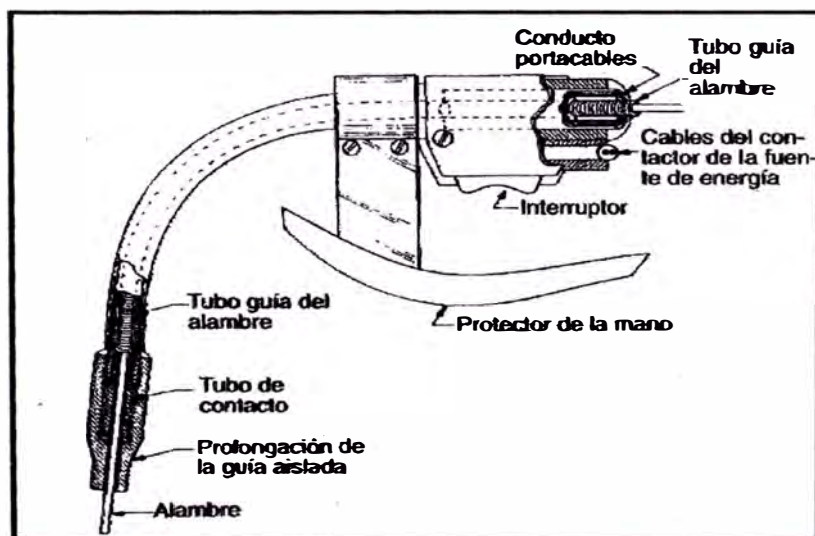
Equipo para el soldeo por arco con alambre tubular
